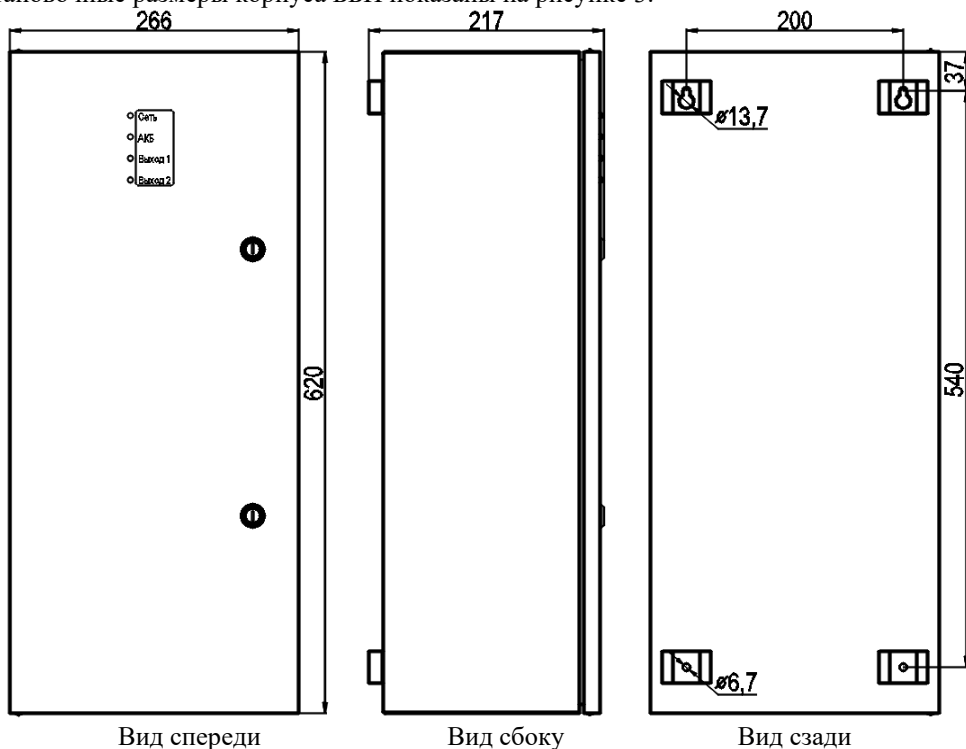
Внешний вид, габаритные и установочные размеры корпуса ББП
